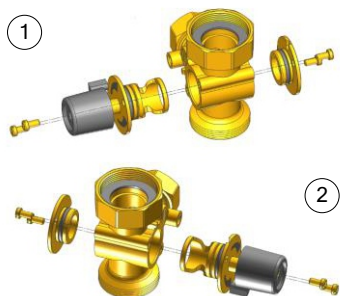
Трёхходовой смесительный клапан (1 - подача справа; 2 - подача слева)
